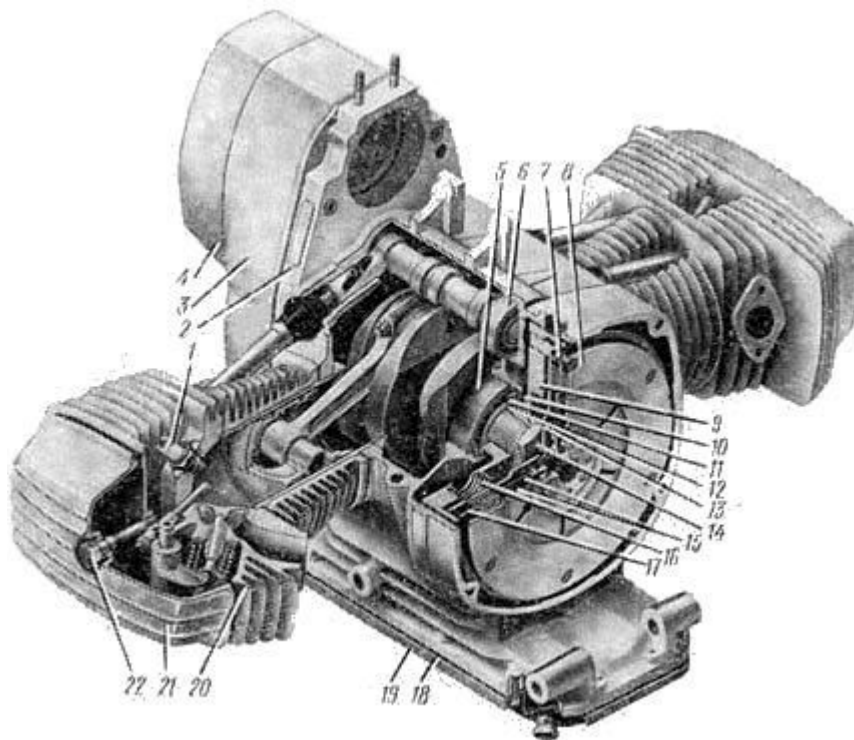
Двигатель МТ-801 (вид со стороны маховика):
